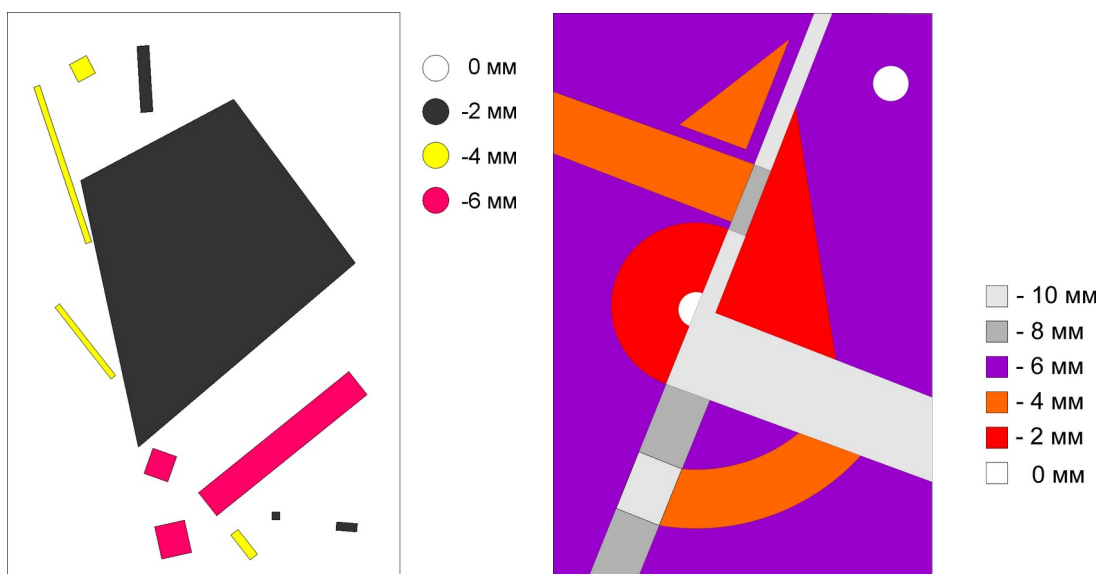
Підготовка ескізу до фрезерування на промисловому обладнанні
